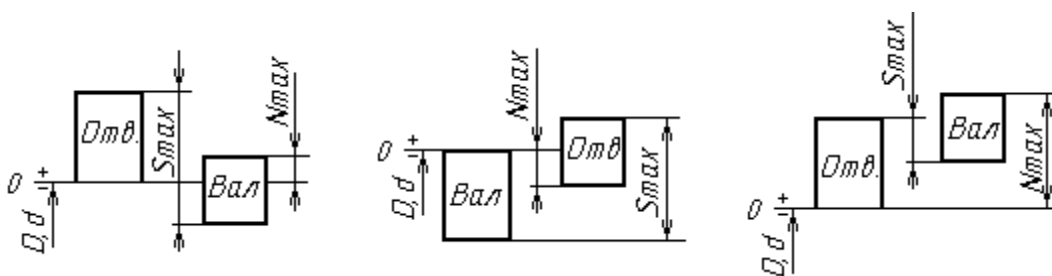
Схемы полей допусков переходных посадок
